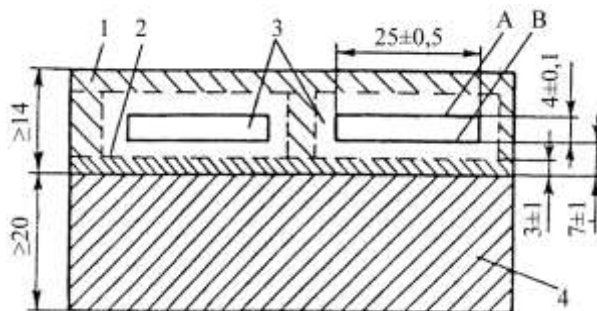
Схема вирізки зразків при випробуваннях наплавленого металу на стійкість проти МКК: 1 - наплавлений метал основного шару; 2 - метал наплавлення підшару; 3 - заготовки для виготовлення зразків; 4 - основний метал (пластина); А і В - поверхні зразка (розміри в мм)
